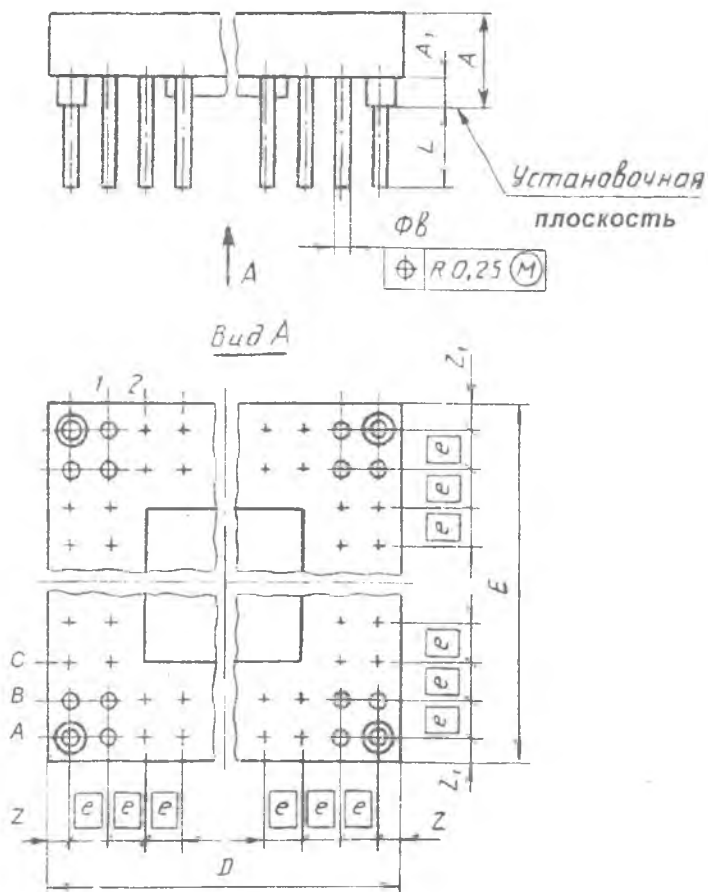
Конструкция корпуса типа 6 подтипа 2
